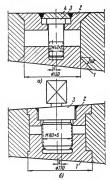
Заглушки монтажных отверстий лопастей рабочего колеса. a- старая кояструкция заглушки; b- новая конструкция заглушки; b- ножияя и верхняя заглушки; b- болт;
